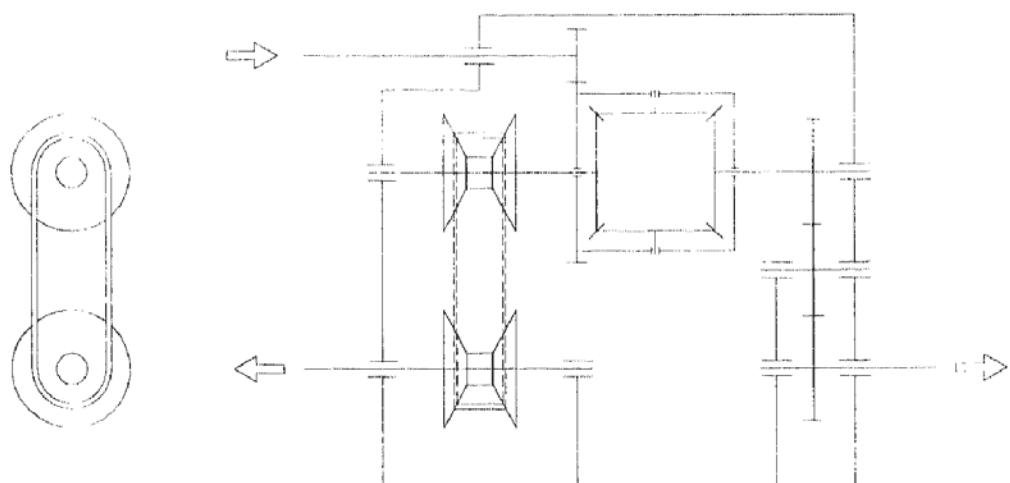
Схема одноступенчатой раздаточной коробки с симметричным дифференциалом и вариатором
